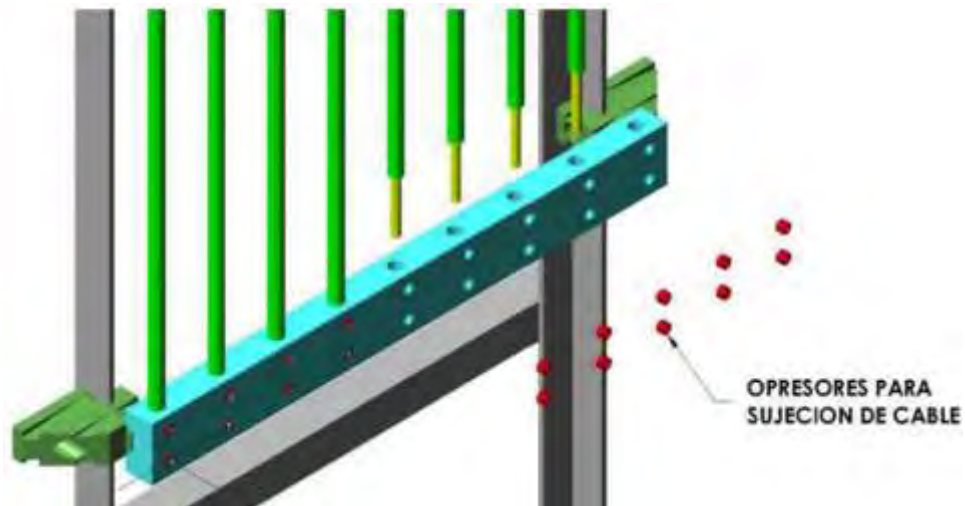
Conexión de los cableados en las barras de acero galvanizado BT2G12C.
